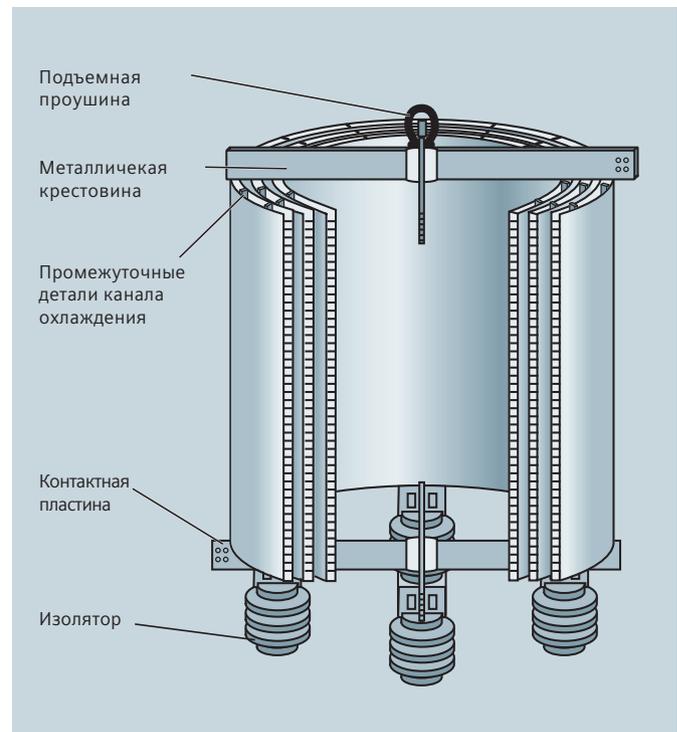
Типовая конструкция токоограничивающего реактора с сухой изоляцией
